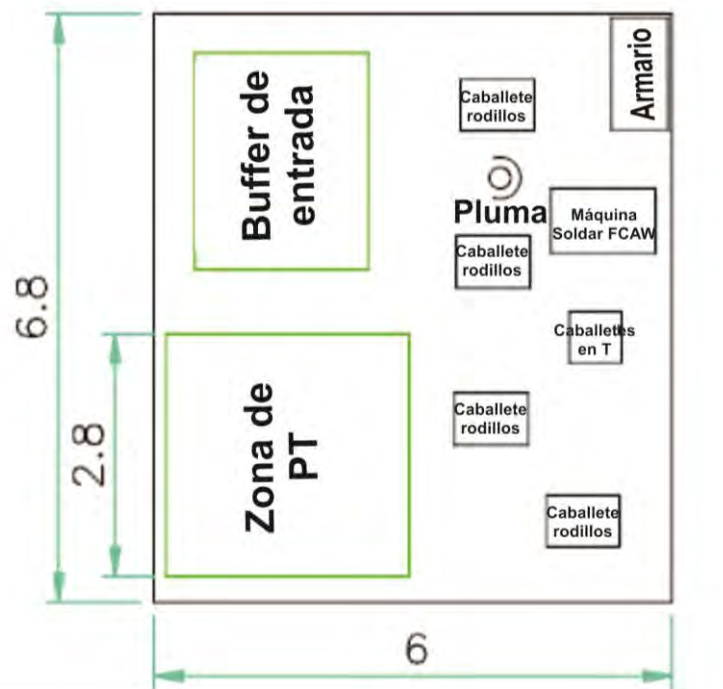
Diseño de estación de trabajo Soldadura Tridimensional – Relleno y acabado
